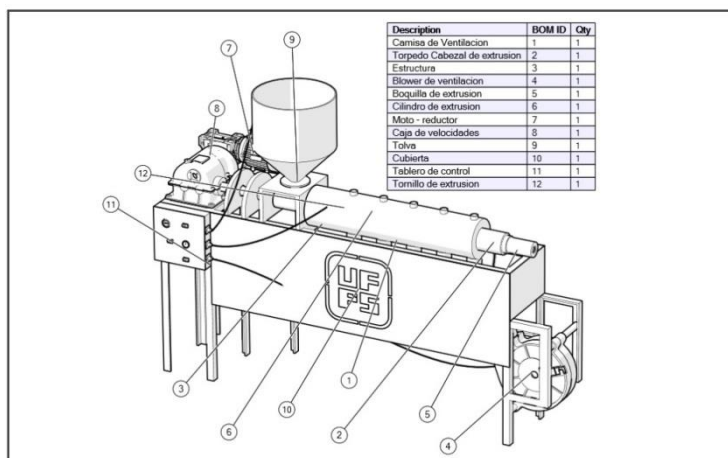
Vista técnica de la máquina extrusora de plástico con sus partes.
